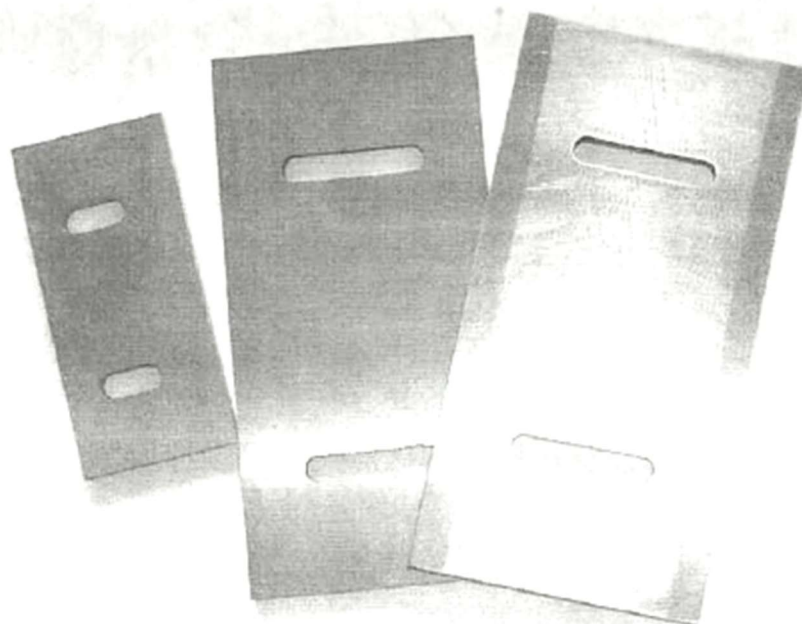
Різці з карбідосталі для обробки дерева
